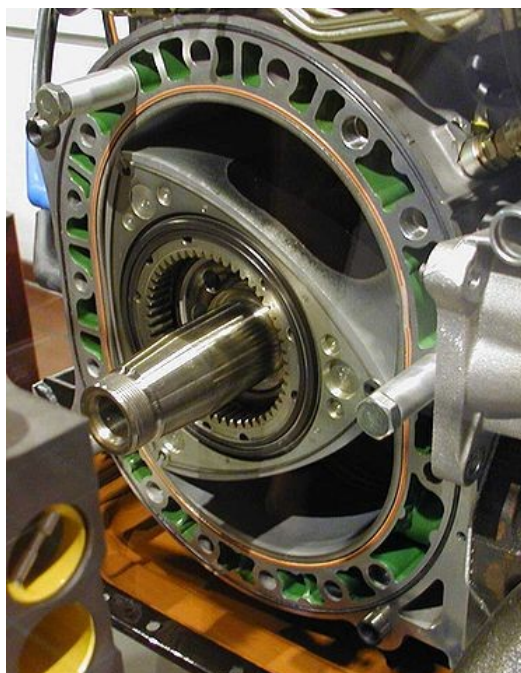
Роторно-поршневой двигатель в разрезе с ротором в форме треугольника Рёло
